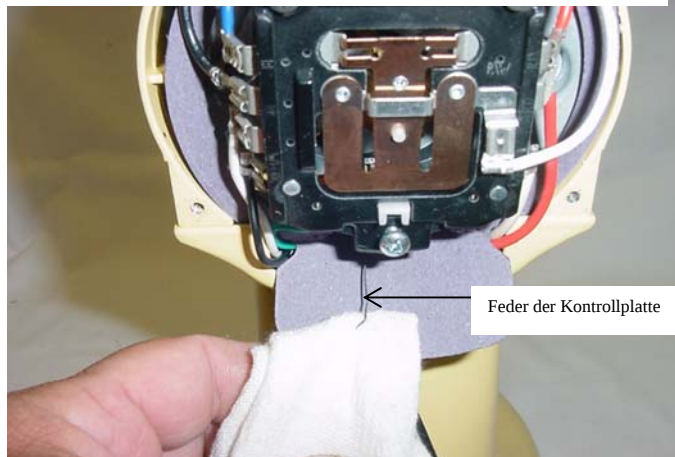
Feder der Kontrollplatte mit einem Tuch sichern, damit sie für den Zusammenbau zugänglich bleibt.
